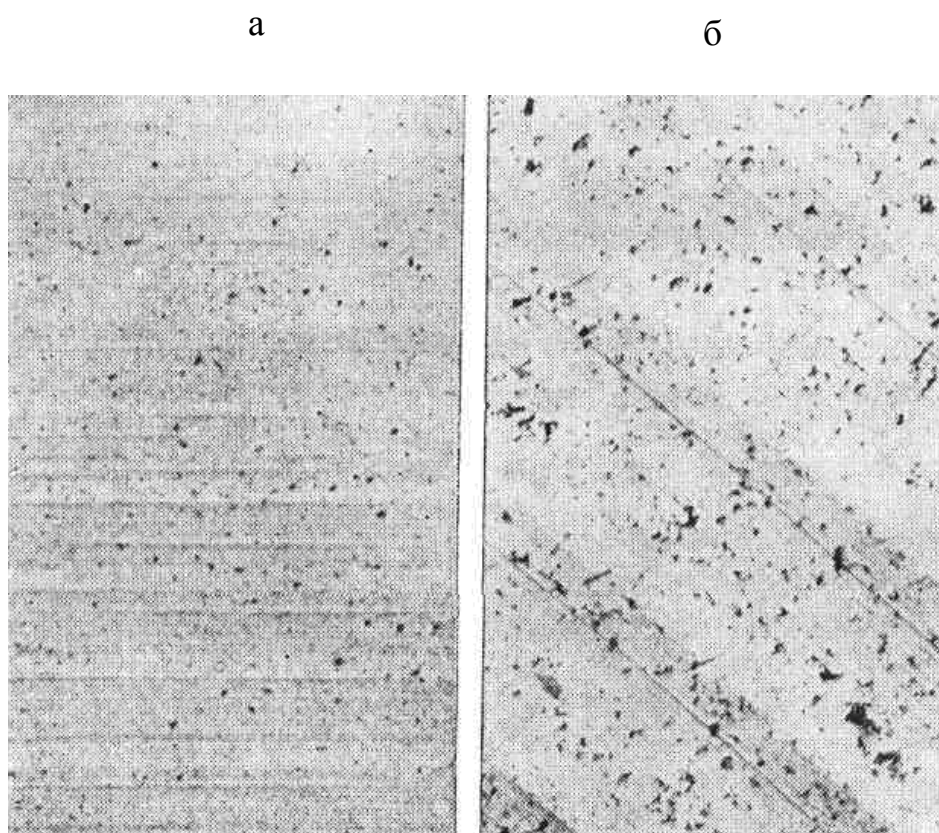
Пористость слитков сплава Д16 после фрезеровки с подачей 7 (а) и 16 мм/об (б)
